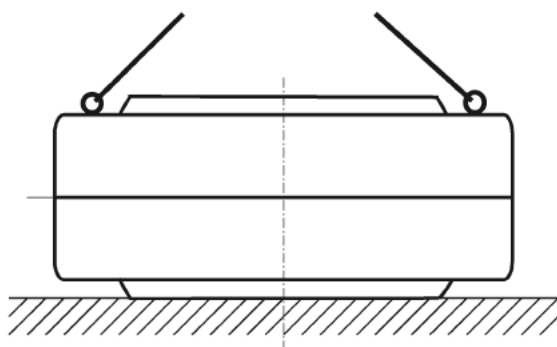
Транспортировка крупногабаритных сферических подшипников скольжения
